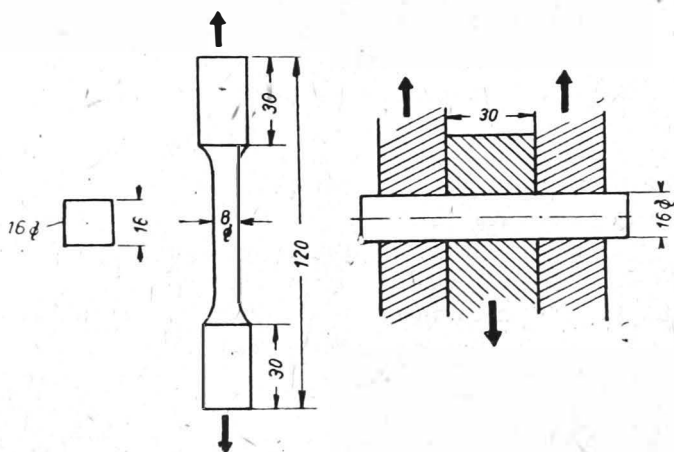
Forma și dimensiunile pieselor de probă din clei folosite de Klemm
